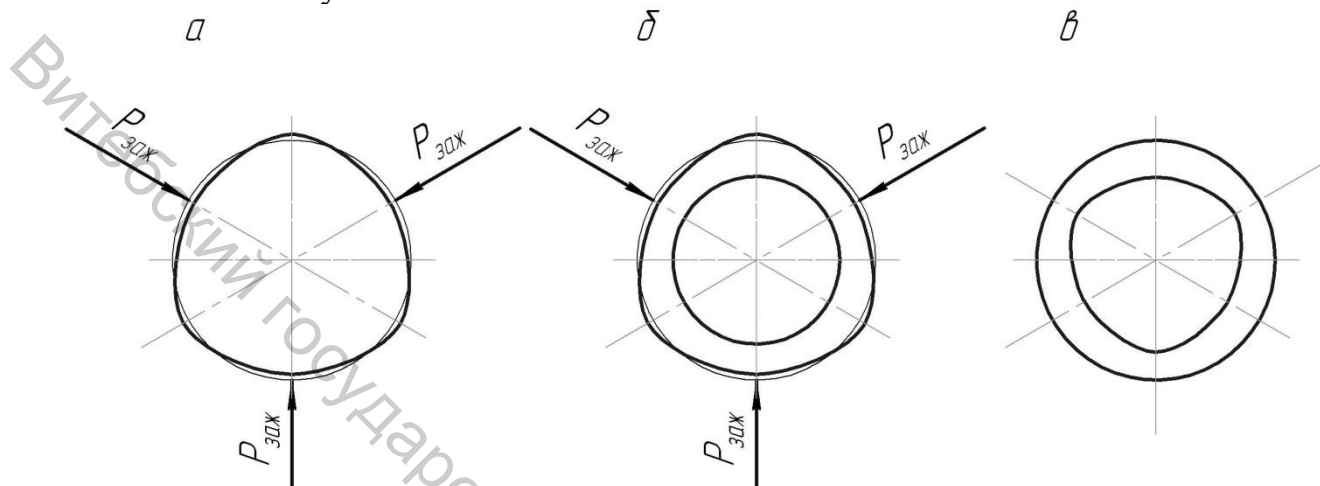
Схема формирования погрешности формы при действии зажимающих сил: а – форма заготовки после закрепления; б – форма расточенного отверстия в закрепленной заготовке; в – форма отверстия после раскрепления заготовки
